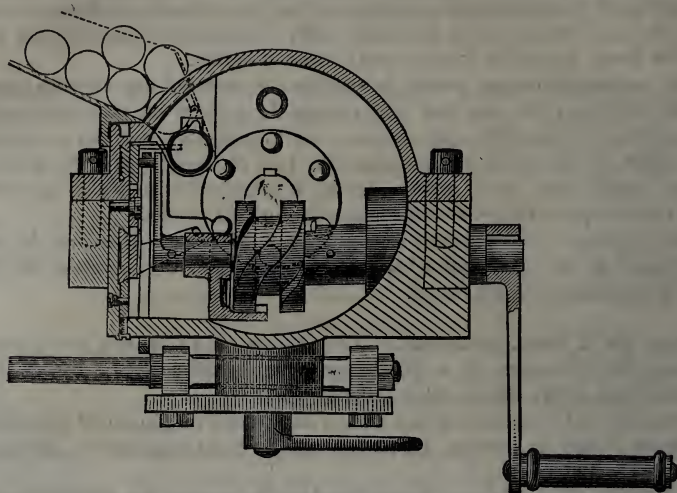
Canon Hotchkiss, vue par l'arrière.
